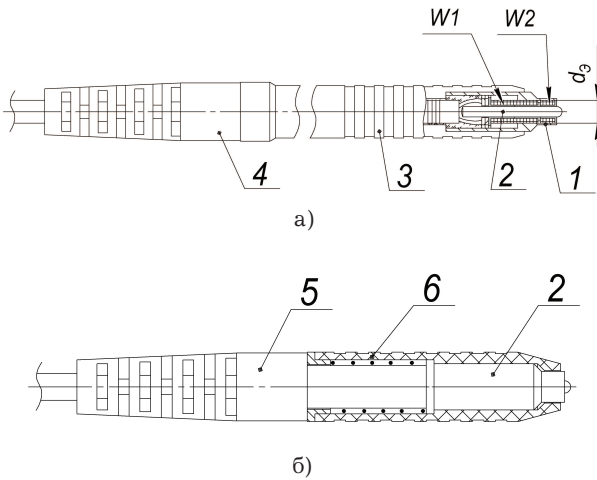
Магнитоиндукционные преобразователи карандашного типа (а) и с подпружиненным установочным корпусом (б): W_1, W_2 – возбуждающая и измерительная обмотки; 1 – корпус – ферромагнитный экран; 2 – сердечник; 3 – наружный корпус; 4, 5 – кабельный ввод; 6 – внешний подпружиненный корпус.
